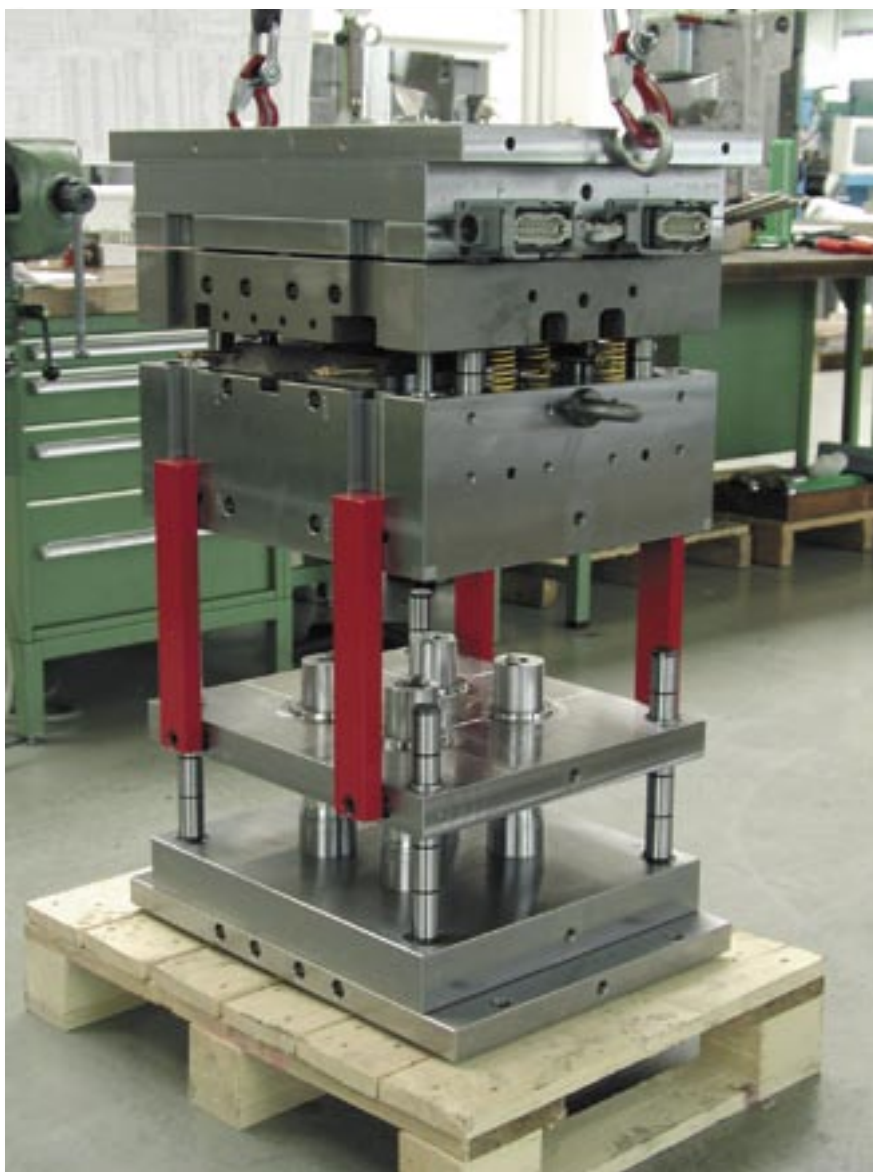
Ein komplettes Werkzeug als Beispiel, gefertigt von der Firma Faßnacht.
